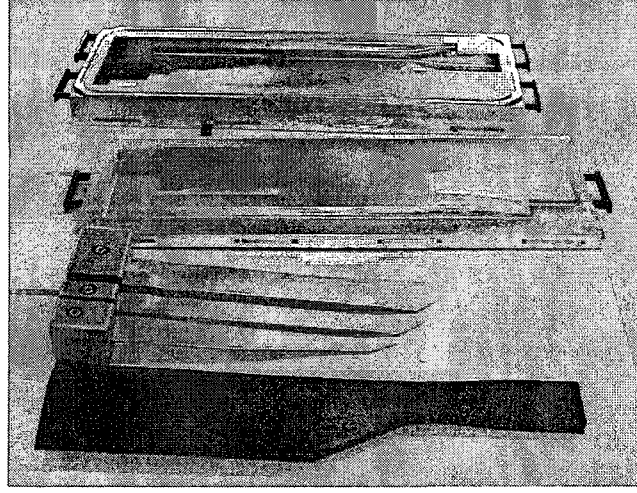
Aerodinamik helikopter karenej bileşeni için takım (Radius Engineering, Inc)
